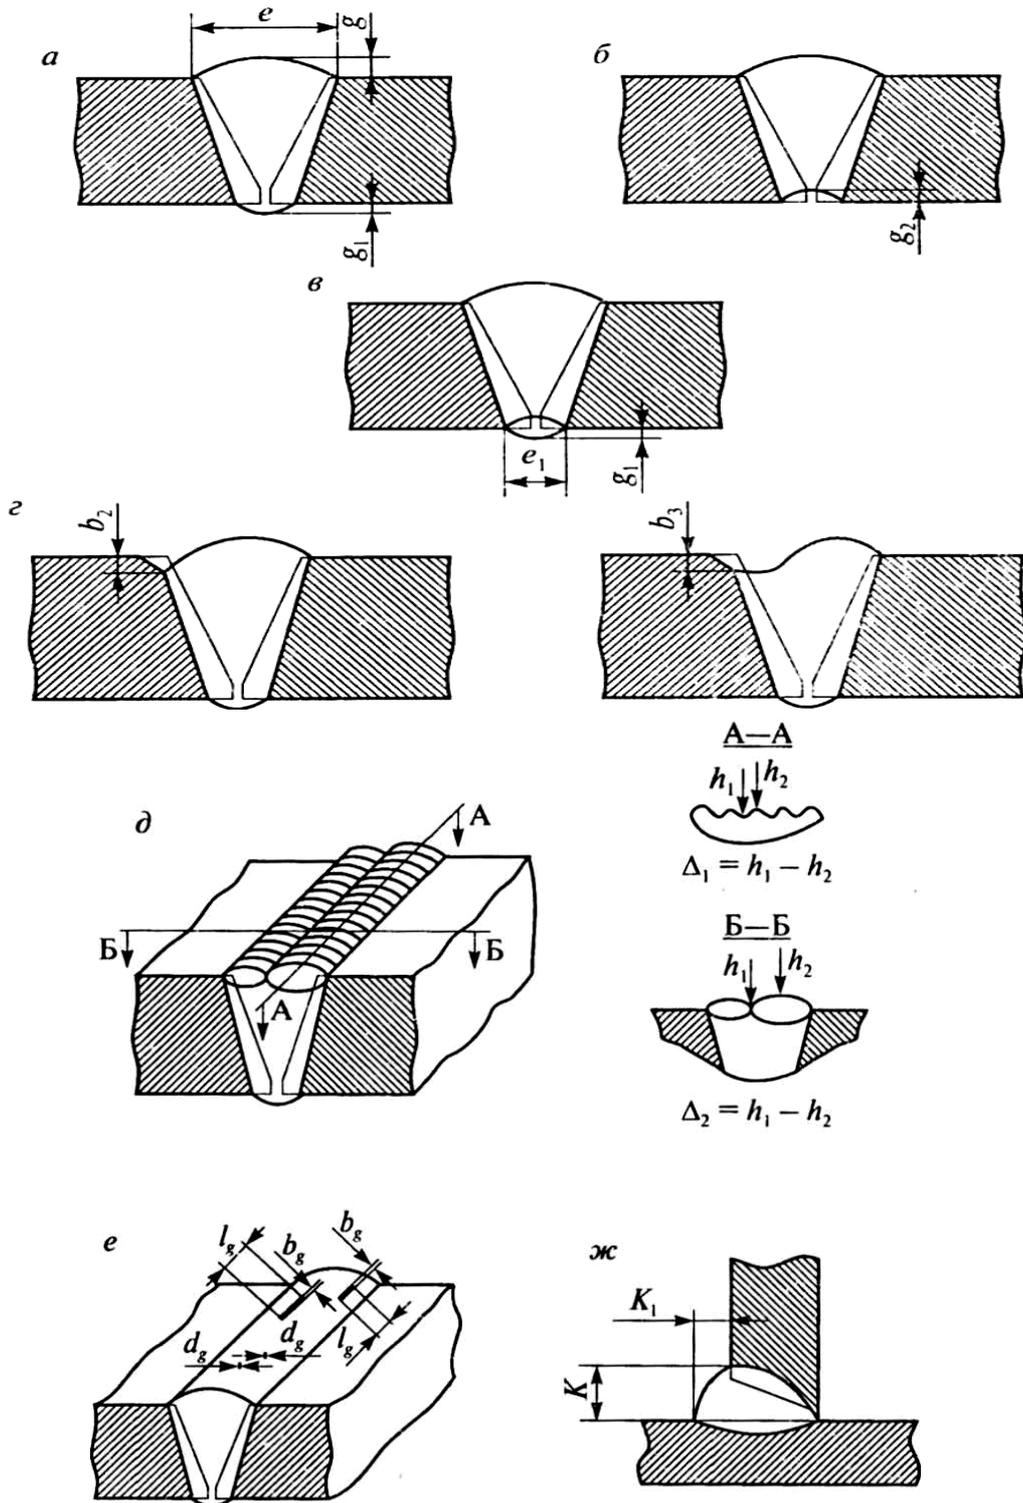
Конструктивные элементы и дефекты сварного шва, подлежащие измерительному контролю: *а, б* – размеры (ширина, высота) стыкового одностороннего шва с наружной и внутренней сторон; *в* – то же двухстороннего сварного шва; *г* – подрез и неполное заполнение разделки кромок; *д* – чешуйчатость (Δ_1) шва и западание между валиками шва (Δ_2); *е* – размеры поверхностных включений (d_g – диаметр; l_g – длина; b_g – ширина включения); *ж* – размеры катета шва углового (таврового, нахлесточного) соединения
